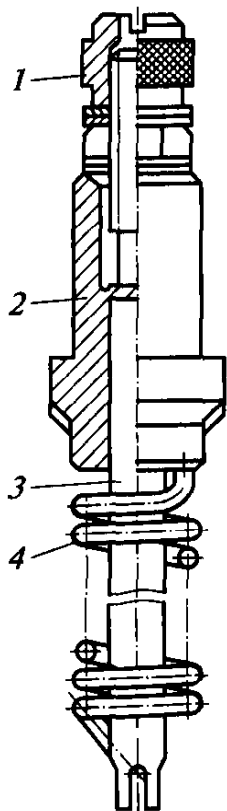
Свеча подогрева впускного воздуха СН-150: 1 — контактная гайка; 2 — корпус; 3 — стержень; 4 — спираль
